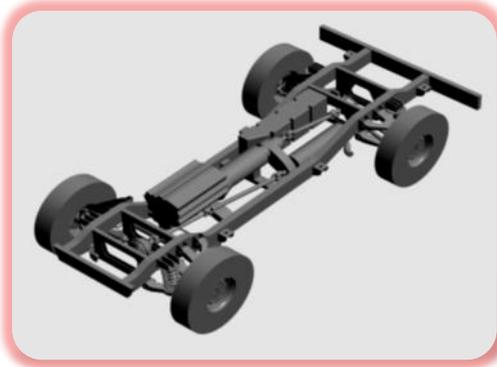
85 Chasis Multicuerpo motor de combustión - motor Híbrido
